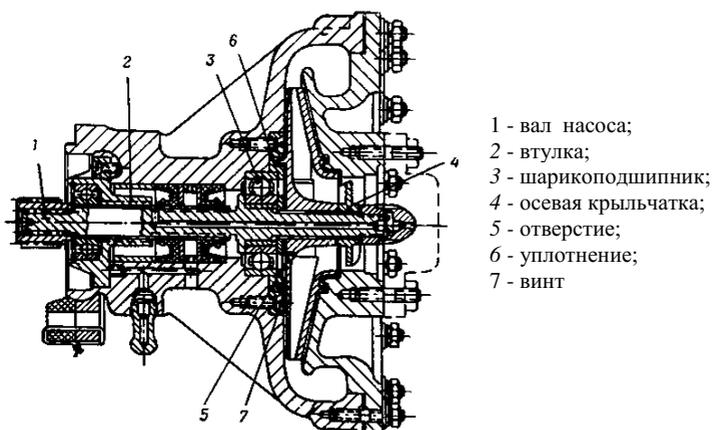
Центробежный насос с крыльчаткой закрытого типа
